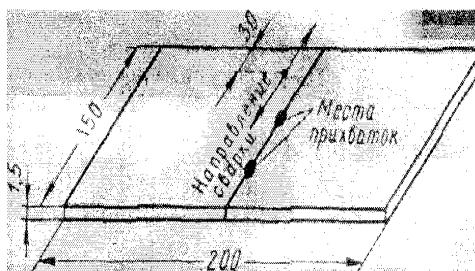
Схема сборки пластин из нержавеющей стали толщиной 1,5 мм
